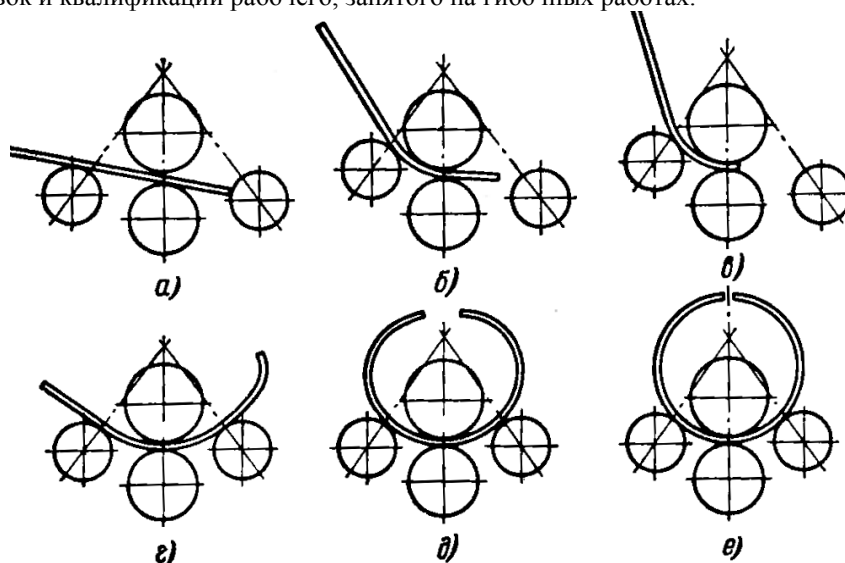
Технология гибки цилиндрической обечайки на 4-хвалковой РЛГМ
